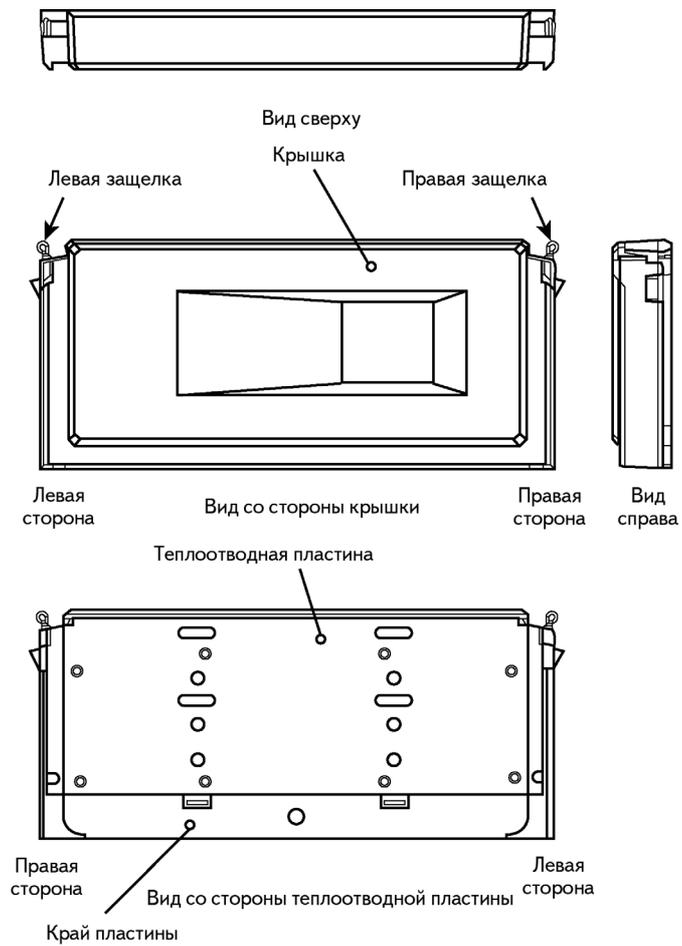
Детали корпуса SEC для процессора Pentium II
